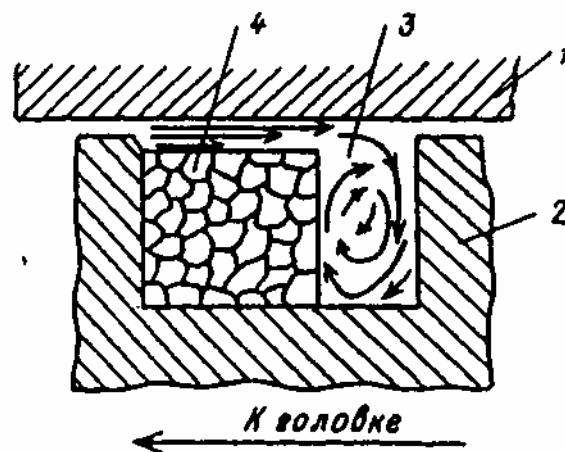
Схема плавления пробки материала в зоне II в межвитковом сечении шнека: 1 – стенки цилиндра; 2 – гребень шнека; 3 – потоки расплава полимера; 4 – спрессованный твердый полимер (пробка) в экструдере
